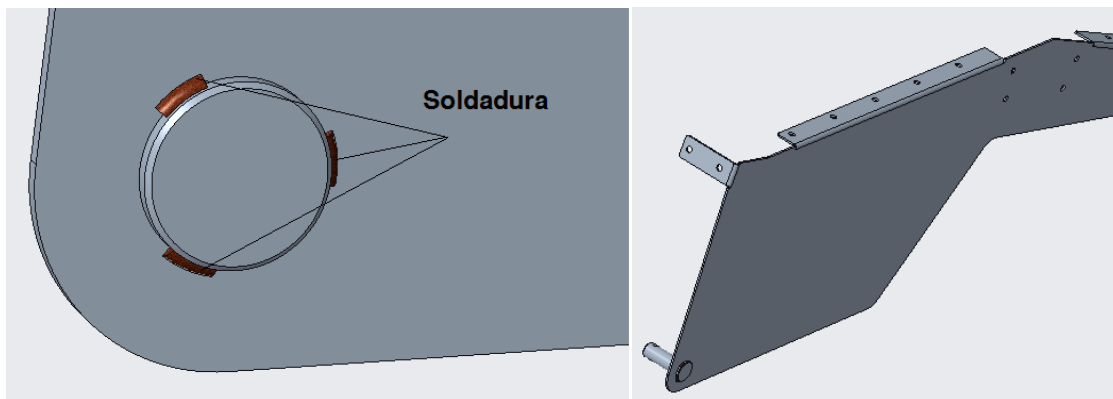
A l'esquerra, detall de la soldadura entre les peces 3, 4 i 6. A la dreta, sentit de muntatge de la peça 6 a les peces 3 i 4. Font: Pròpia
